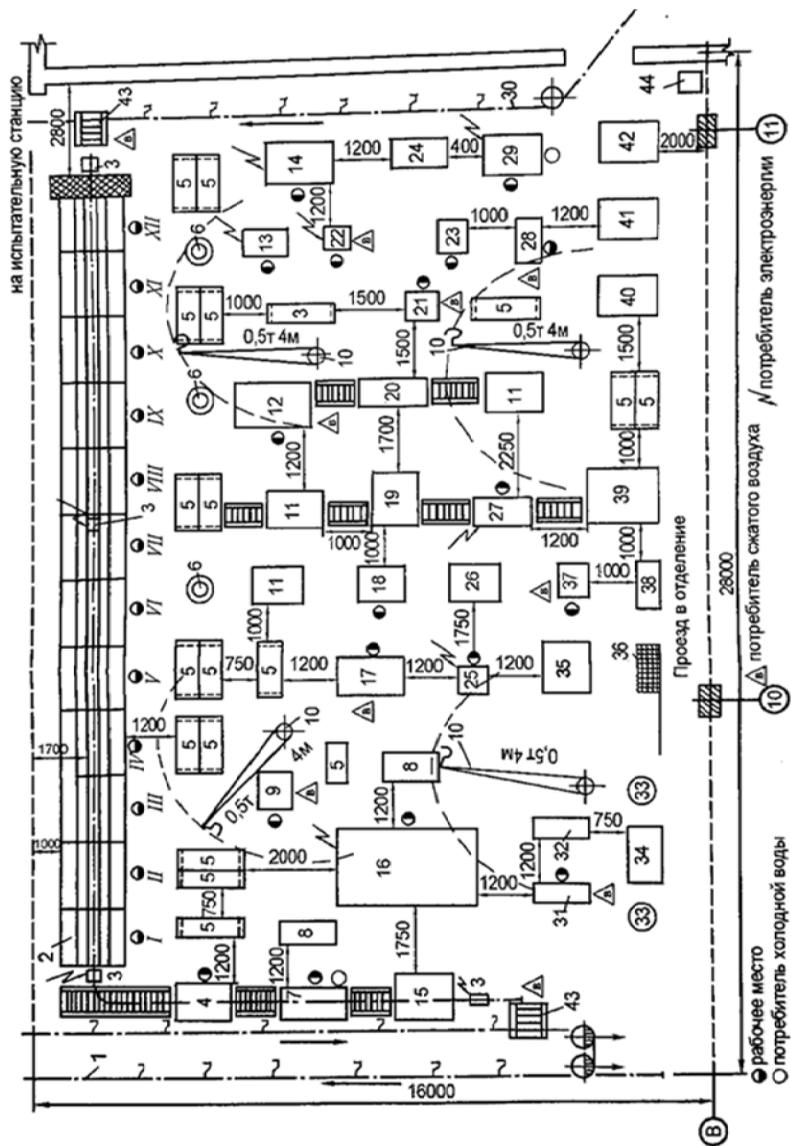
Планировка участка сборки двигателей предприятия для ремонта силовых агрегатов грузового автомобиля ГАЗ
